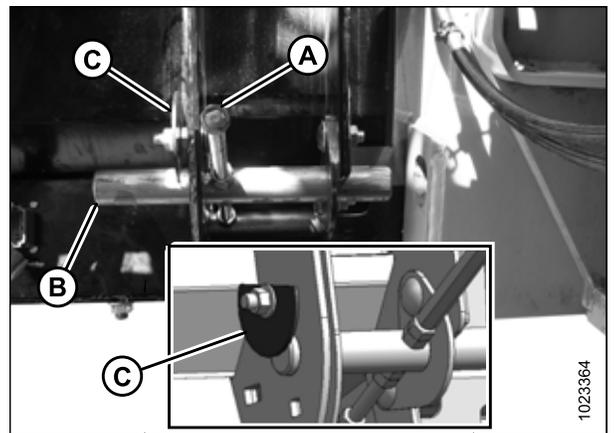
Desacoplamiento del cardán para cosechadora
